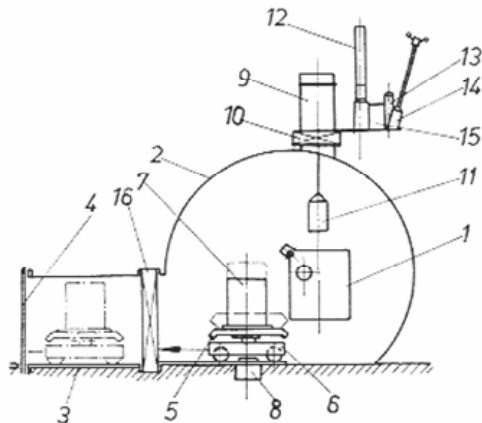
Schema principală a instalației de topire prin inducție în vid 50/80 kg de fabricație Consarc Engineering Ltd.
